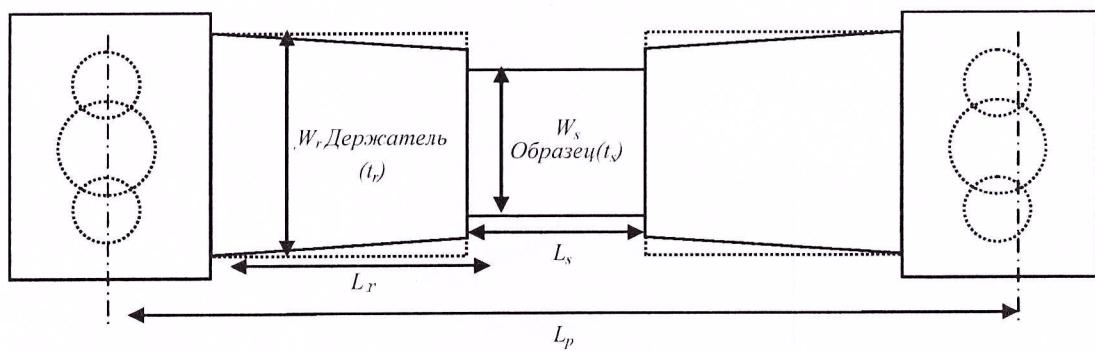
Схема расположения испытываемого образца, держателя и оснастки
